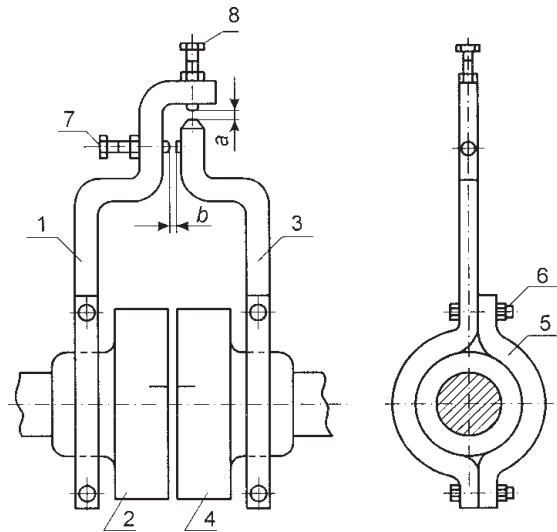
Центровочные скобы: 1 — наружная скоба; 2 — полумуфта; 3 — внутренняя скоба; 4 — электродвигатель; 5 — хомут; 6, 7, 8 — болты
